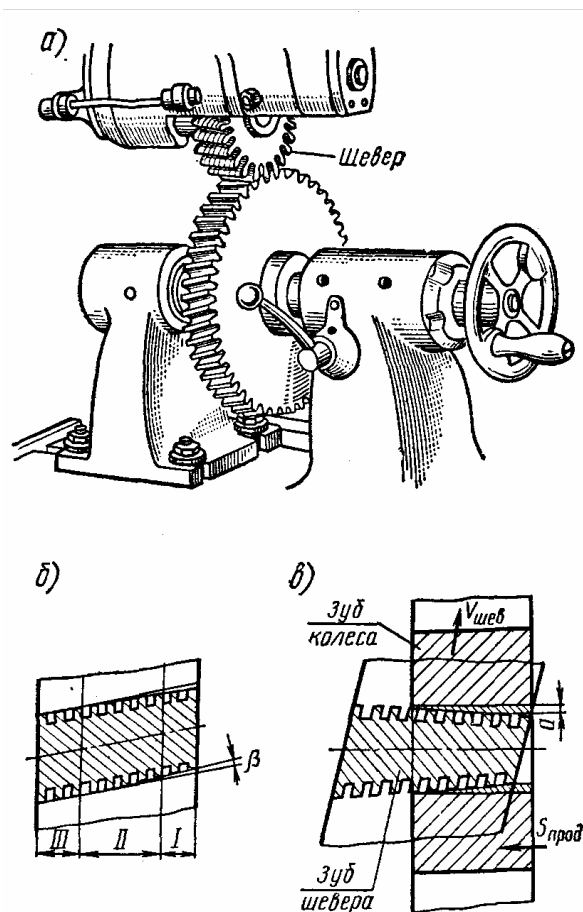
Шевингование цилиндрического зубчатого колеса дисковым шевером: а – общий вид; б и в – схема шевингования за один проход
